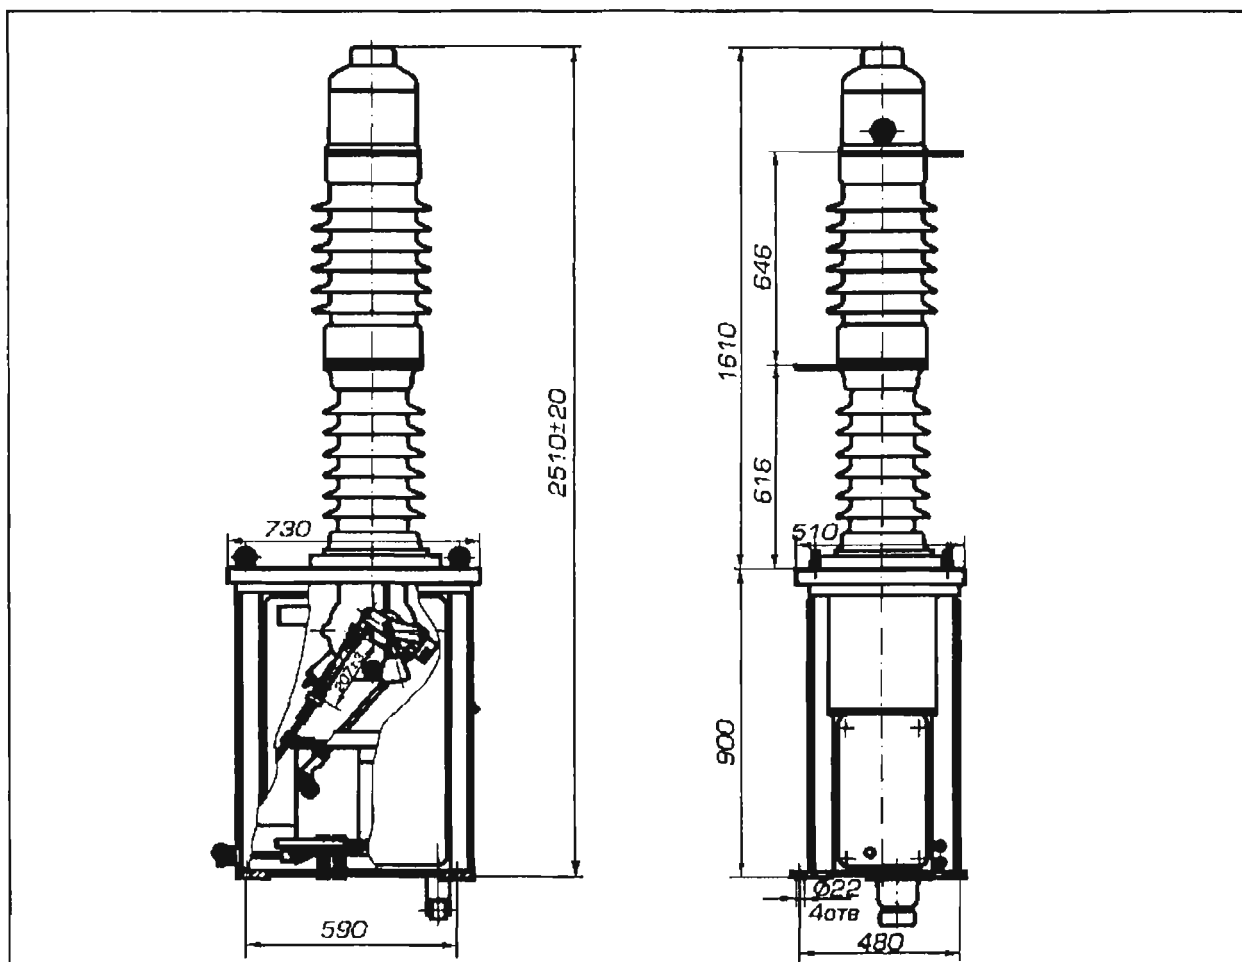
Габаритные размеры выключателя ВВК-27,5
